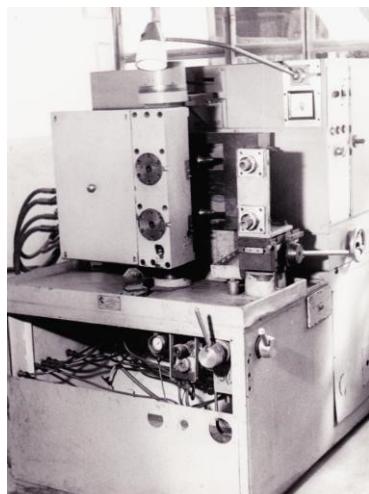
Внешний вид станка модели МЗ-38 для одновременного восстановления двух долотчатых коронок
